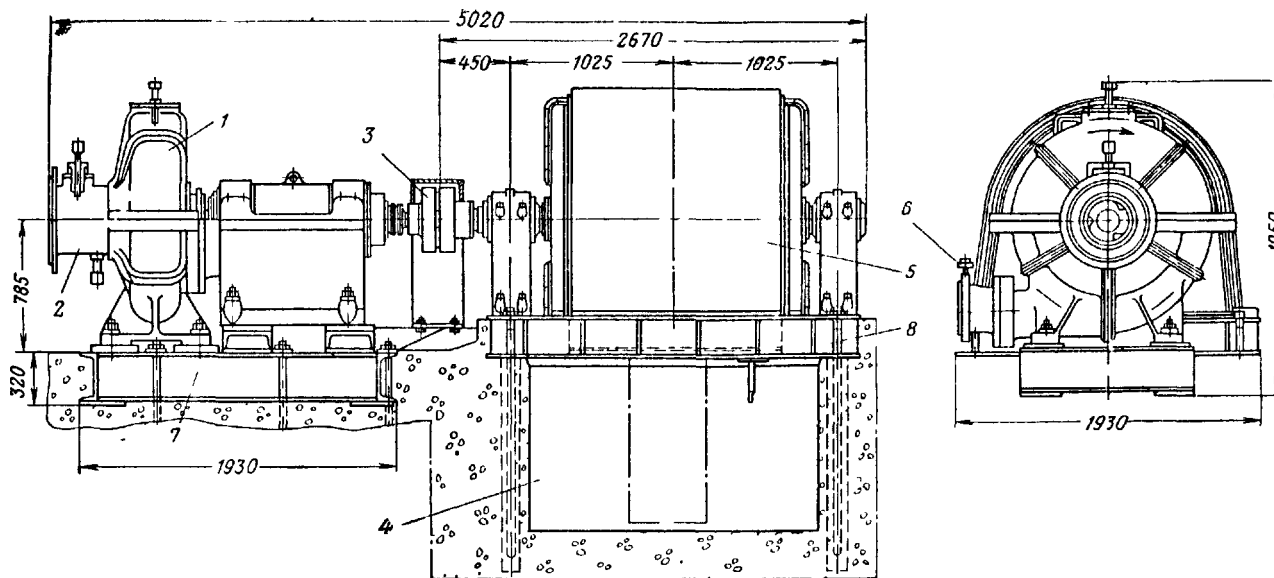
Общий вид установки углесоса 14У-7:
